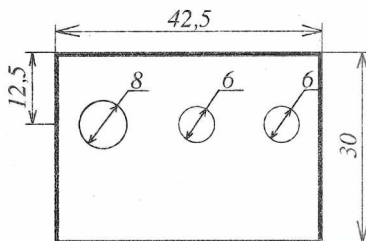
Задняя стенка корпуса (вид снаружи корпуса).
